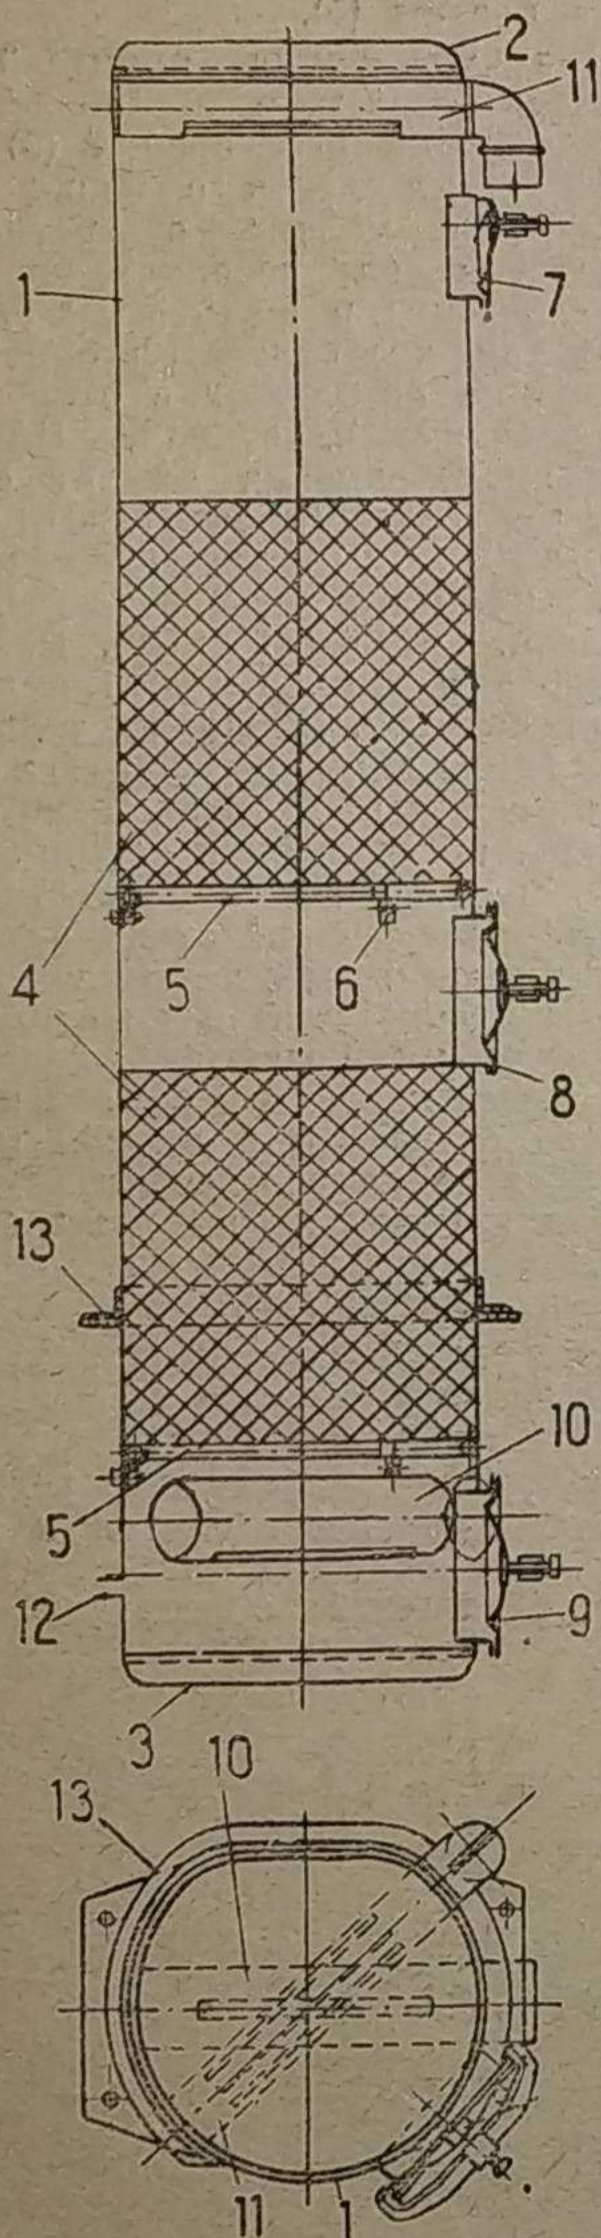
Вертикальный очиститель тонкой очистки газа установки ЗИС-21
